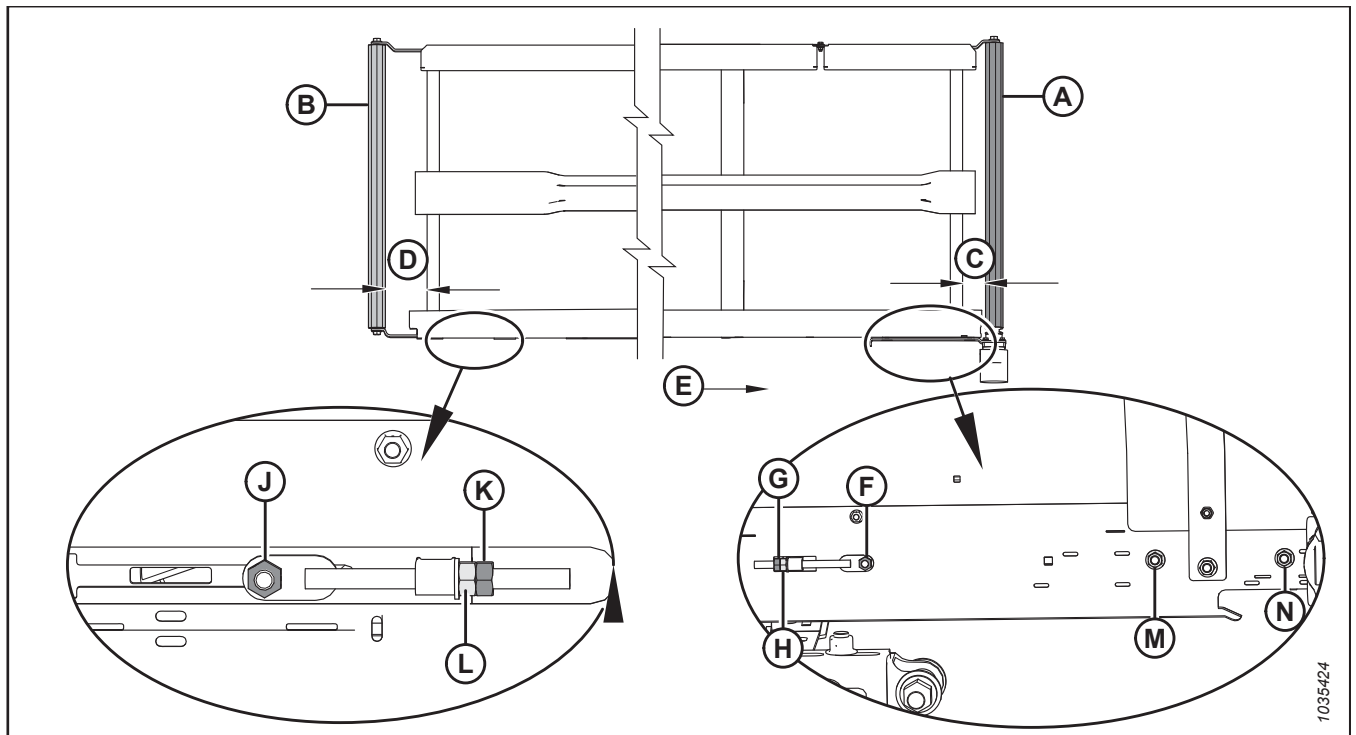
Réglage de l'alignement du tapis – Tapis gauche
